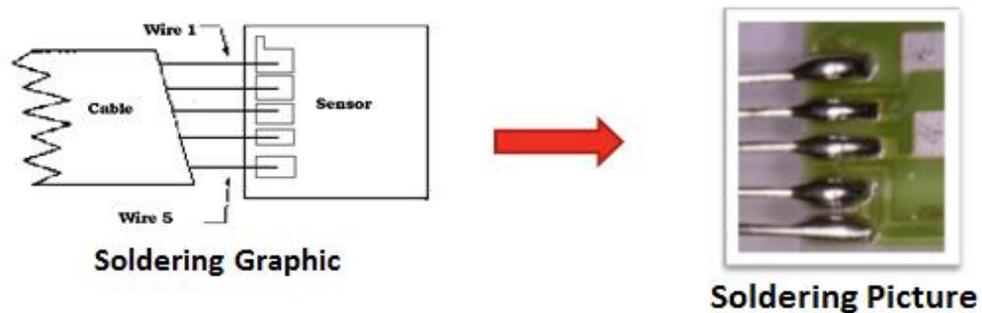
soldadura del sensor al cable del DPT.⁸
